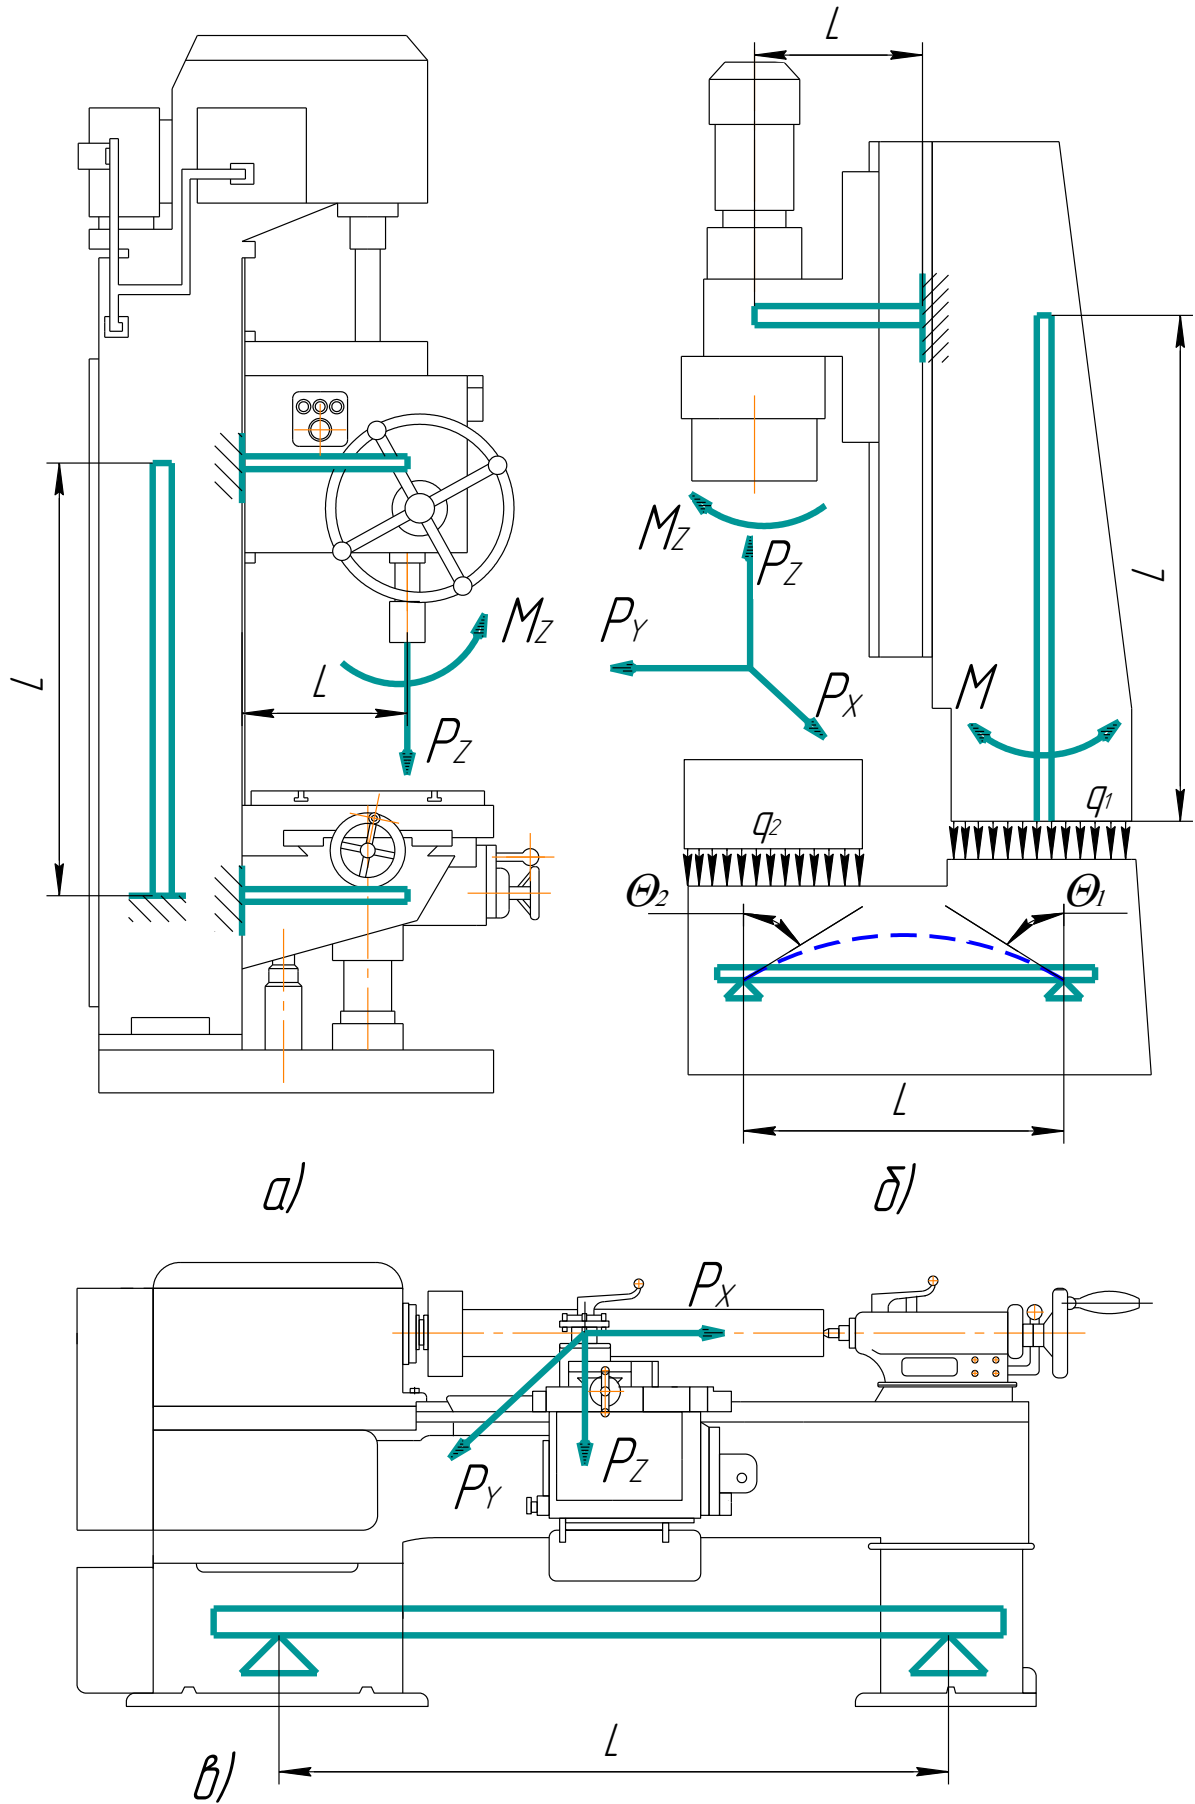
Розрахункові схеми, базових деталей верстатів: а) - свердильного; б) - багатоцільового; в) токарного
